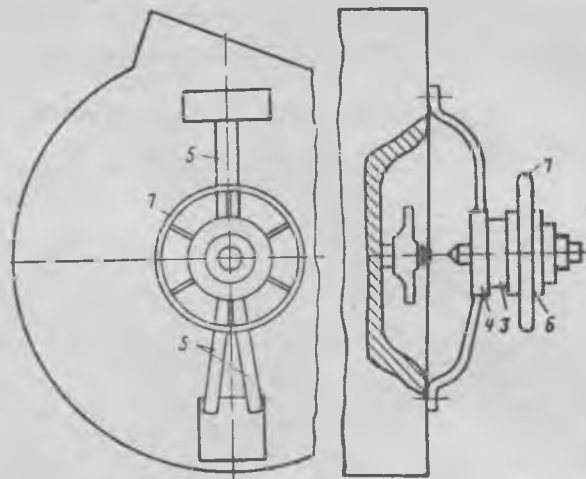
Установка подвижного центра на тяговом двигателе. Обозначения те же, что на рис. 3
